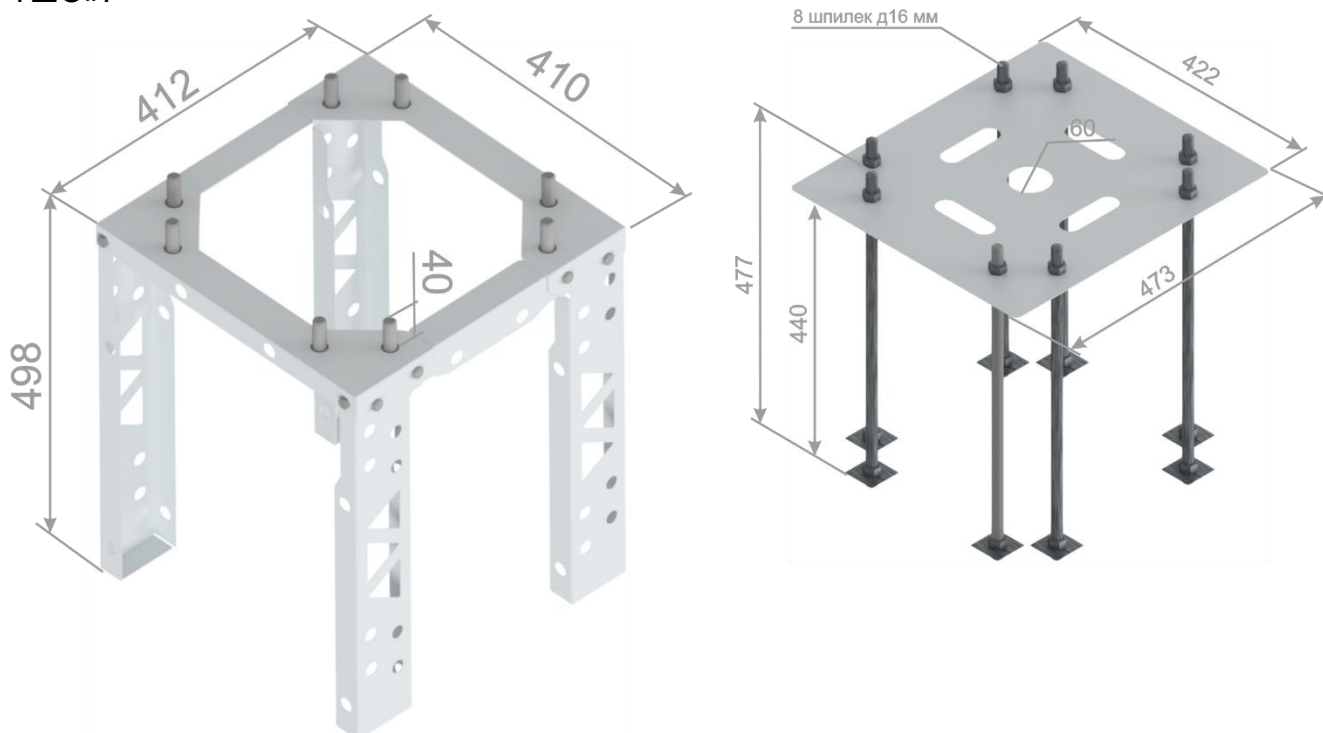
Габаритный чертеж монтажных пластин.
